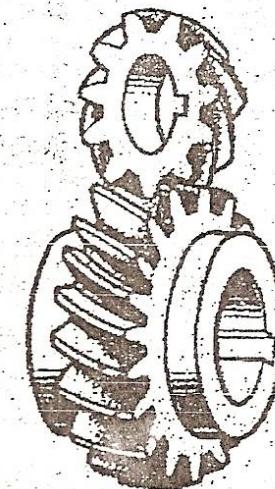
Engranajes cilíndricos helicoidales para ejes que se cruzan
